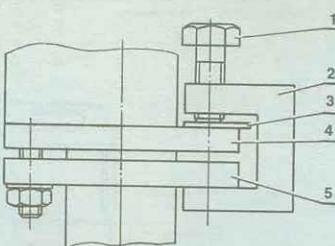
Установка скобы: 1 — болт; 2 — скоба; 3 — пластина; 4 — фланец головки цилиндров; 5 — фланец приемной трубы
